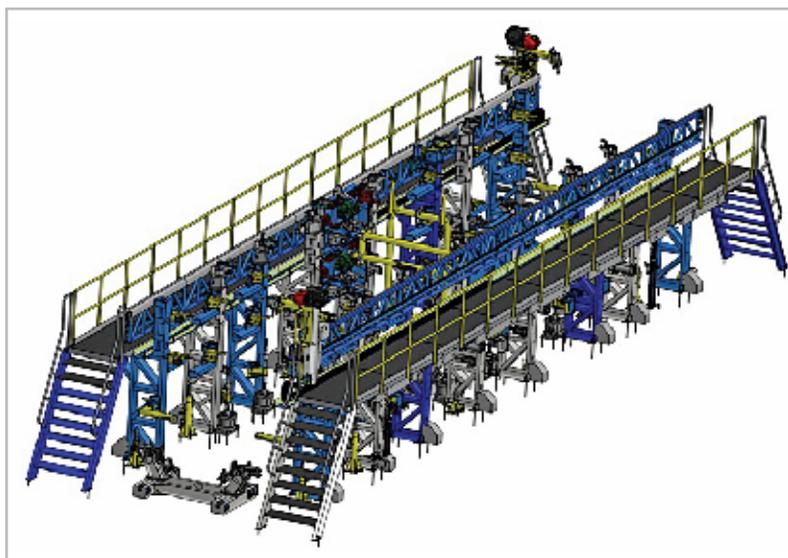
Общий вид универсального стенда сборки каркасов кузовов.
